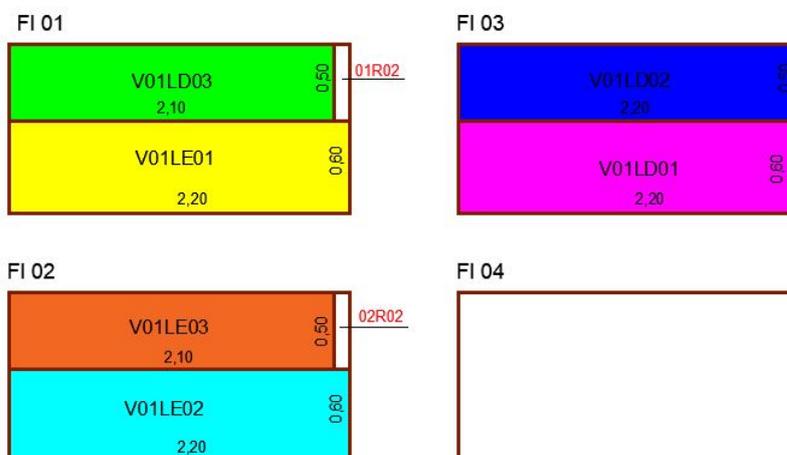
Diagramação do plano de corte depois do aproveitamento de primeira ordem.
